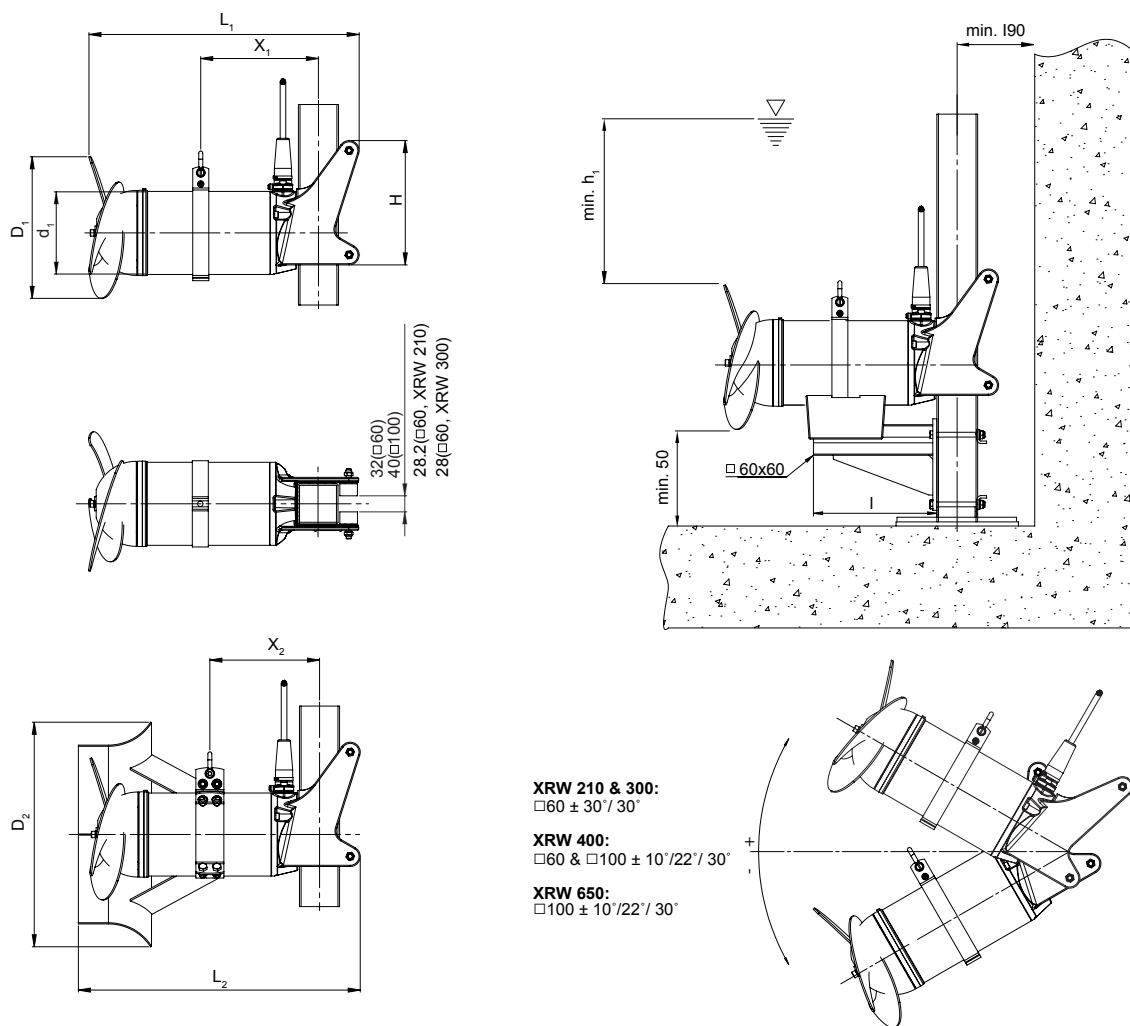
Dimensioner XRW 210 - 900 monterad på skena
